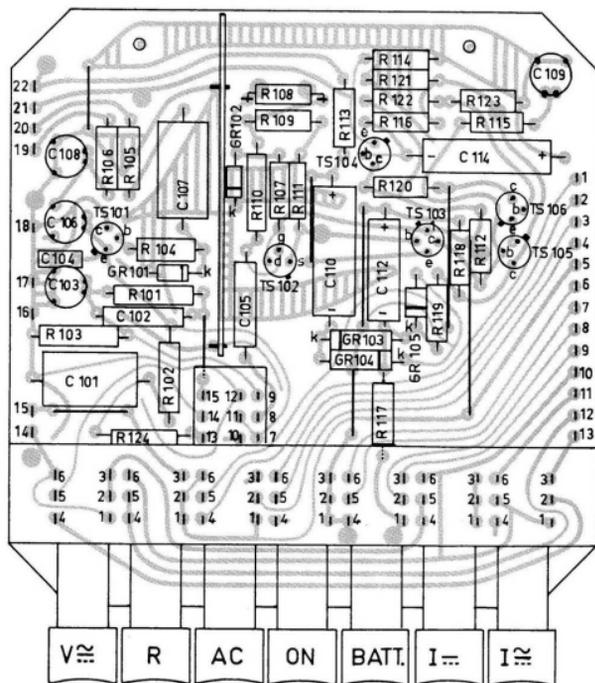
Vue de dessous (platine de câblage imprimé U2 rabattue)
